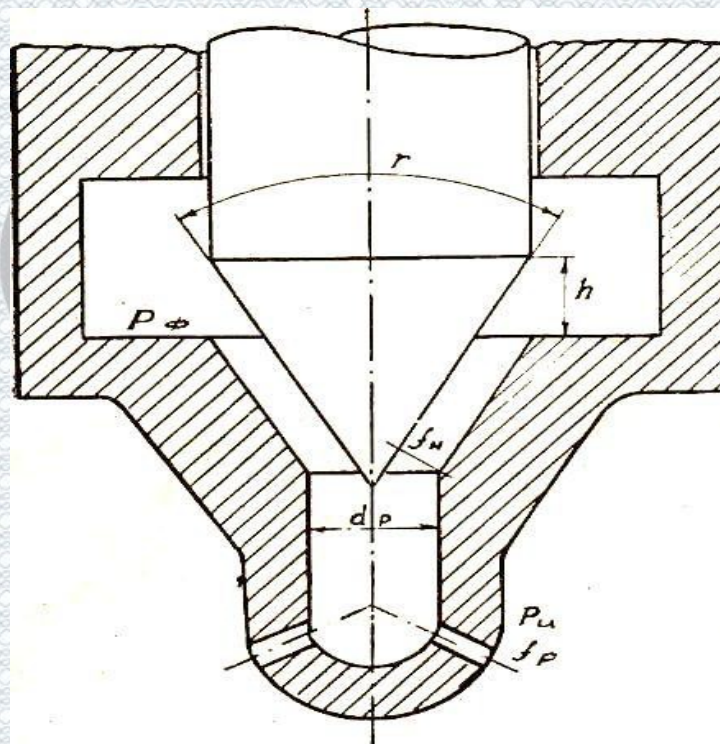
Розрахункова схема клапанів керування форсункою
